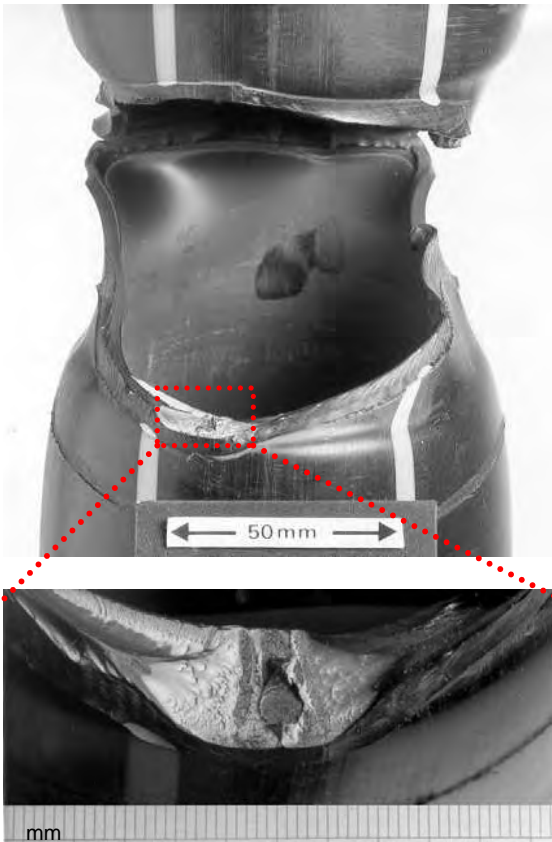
Fotografías de una soldadura que falló en una tubería de 125 mm de diámetro, que contiene un defecto planar de 4 mm de diámetro.
